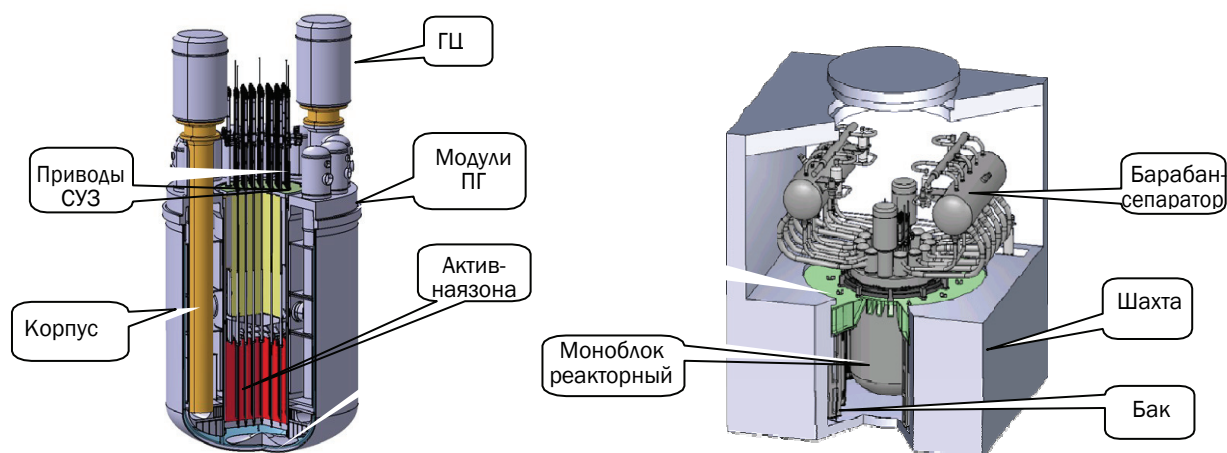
Реакторный моноблок и компоновка оборудования РУ СВБР-100
